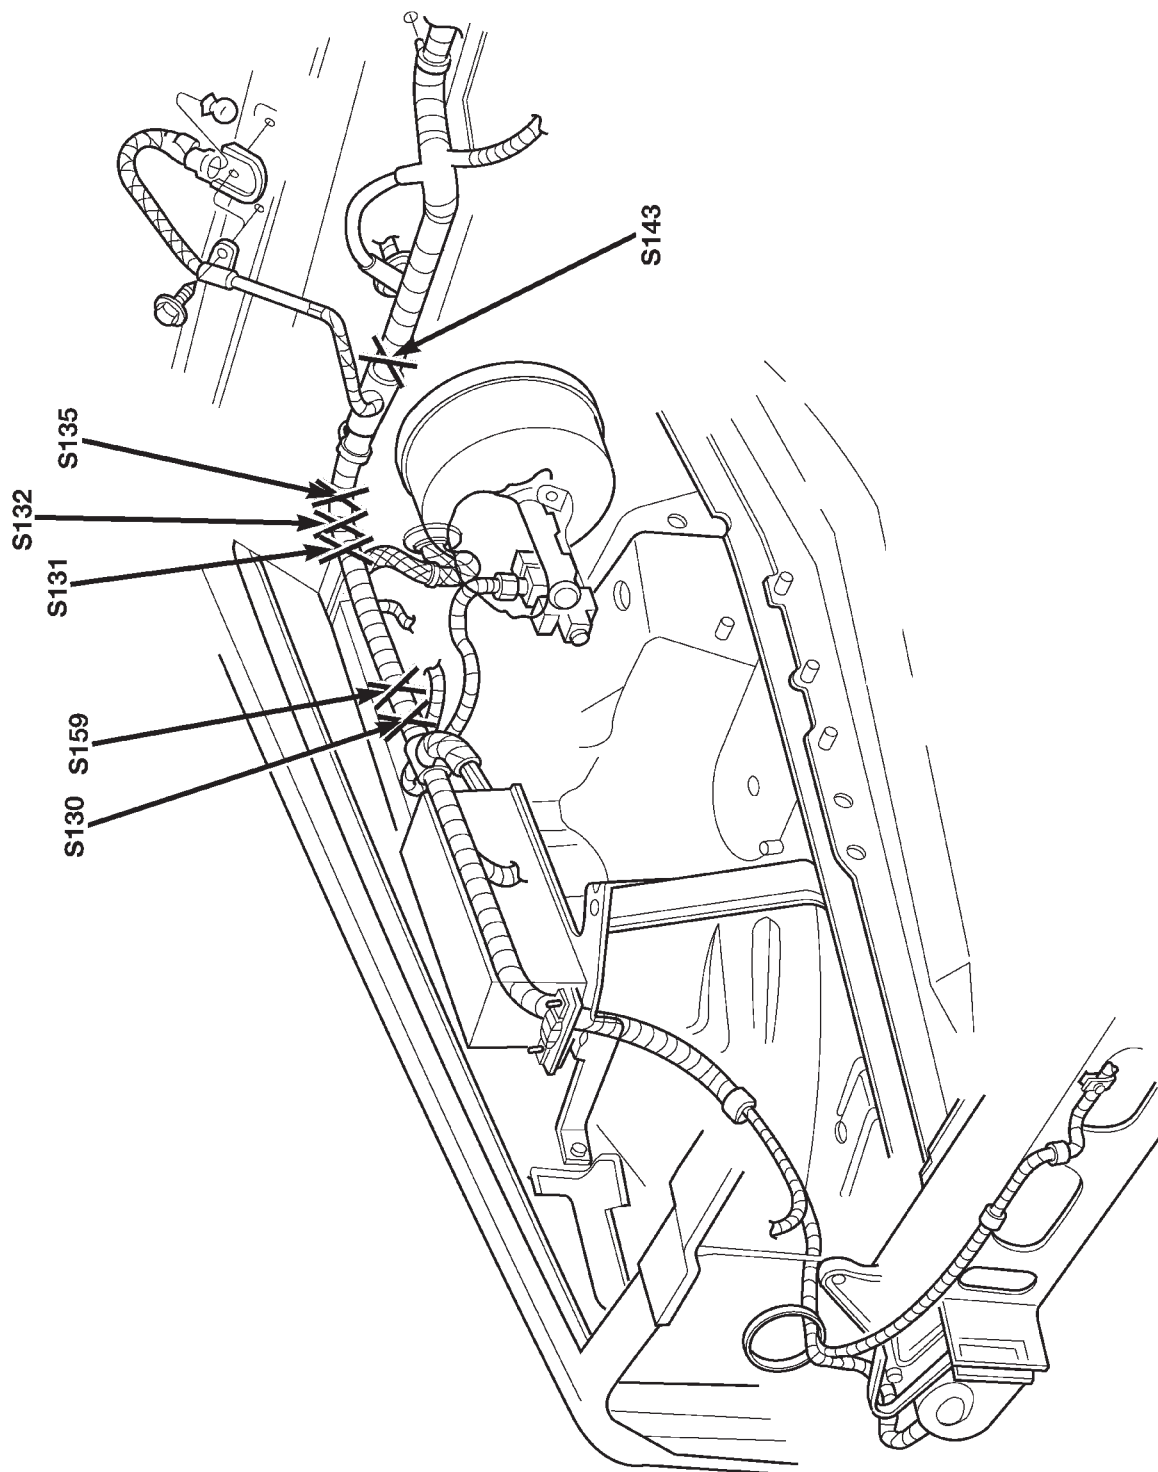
Kabelverbindungen Motorraum rechts—2.5L-Motor Rechtslenker
